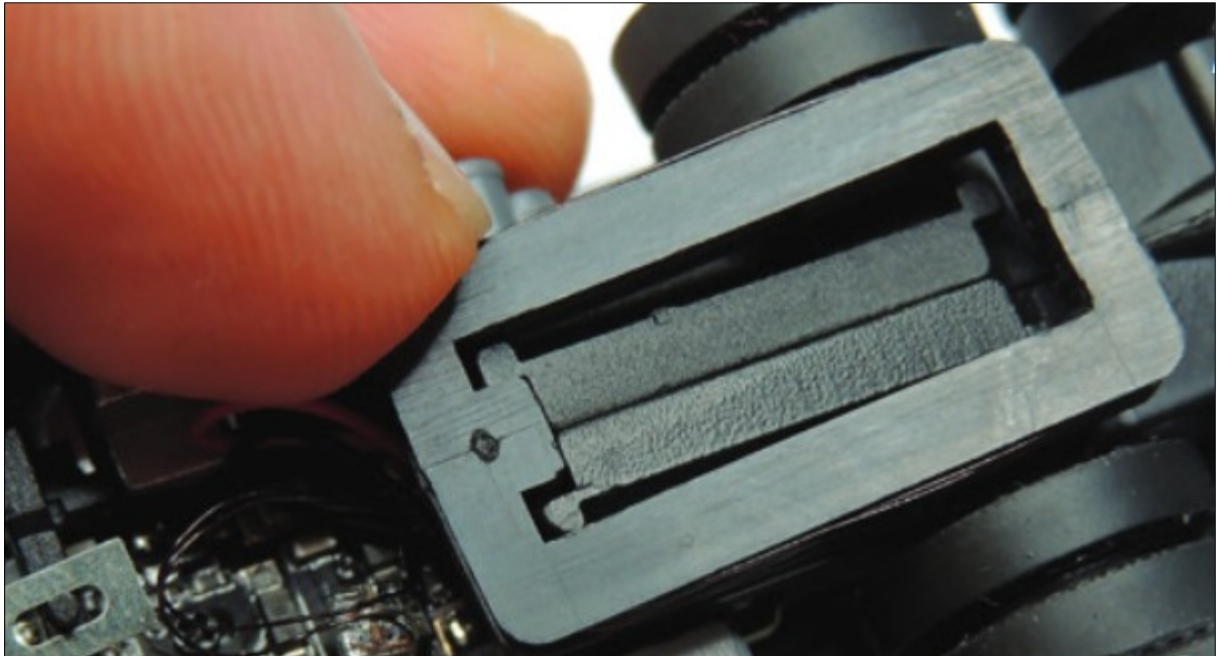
Aufstecken der „Empfängerspule“ auf das Getriebe
